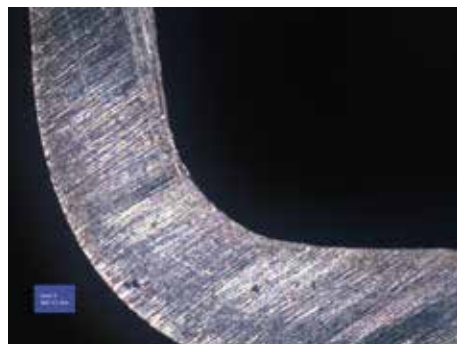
Aufnahme Werkstück- Werkzeuginnenradius bei 700 bar Innendruck
